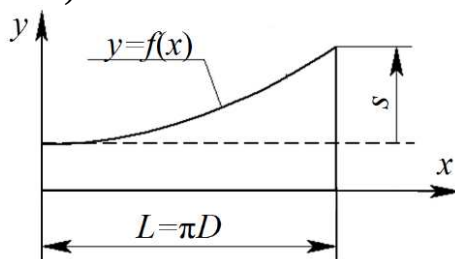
Развертка профиля цилиндрического торцового кулачка
